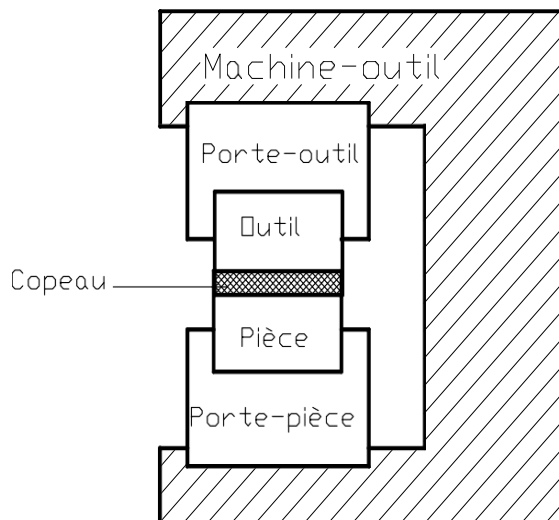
Schéma des éléments dans l'action d'usinage [2]
